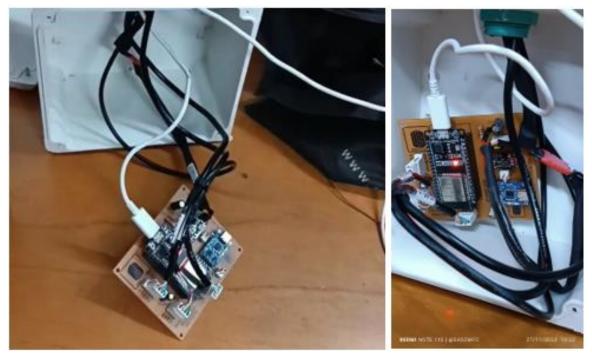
Ensamble y cableado para la PCB & sensores de la estación meteorológica.
